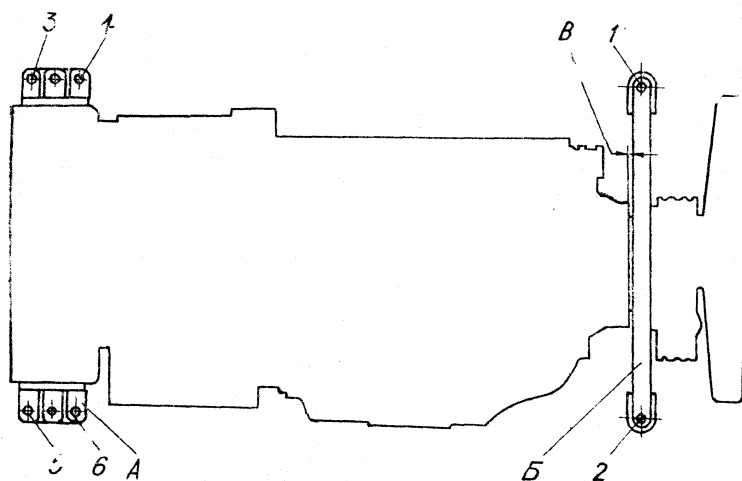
Схема расположения лап опор дизеля 1Д6-150.
